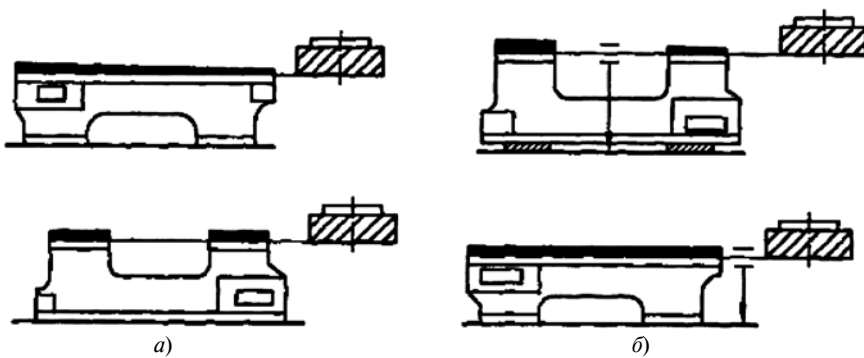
Базирование ножками (а) и направляющими (б) станины токарного станка на первой операции
